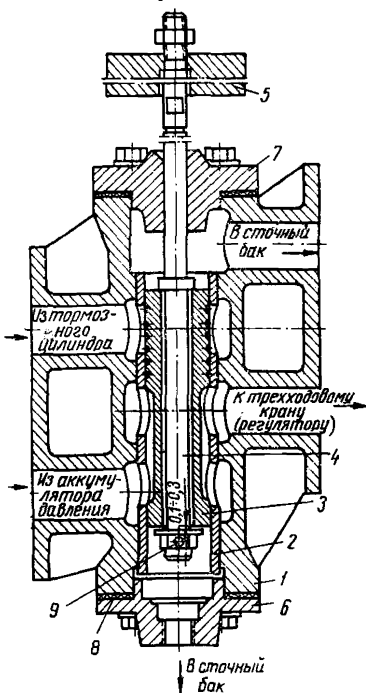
Четырехходовой кран: 1 — корпус; 2 — втулка; 3 — золотник; 4 — шток; 5 — груз; 6 и 7 — крышки; 8 — прокладки; 9 — шплинт
